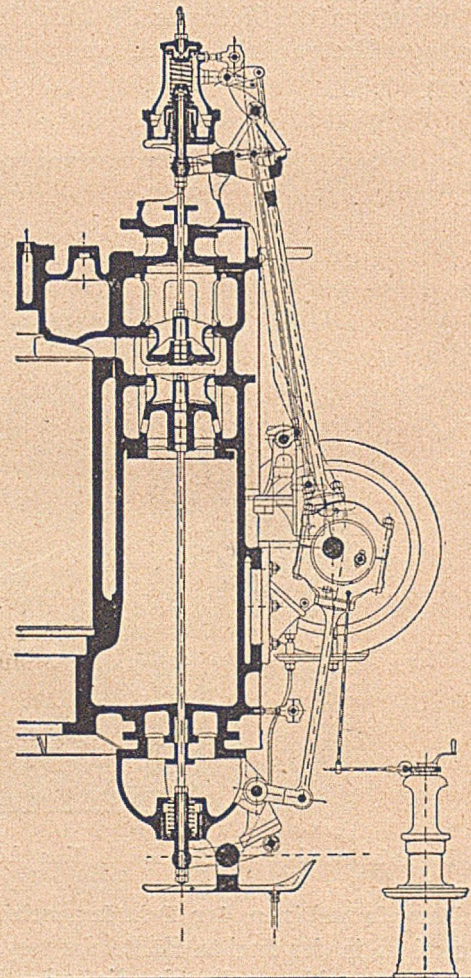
Steuerung des Hochdruckzylinders der Nürnberg-Augsburger Maschine.
